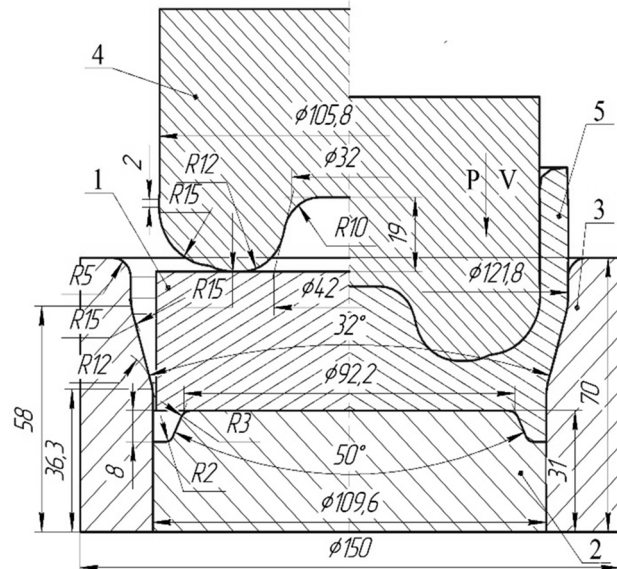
Схема зворотного видавлювання: 1 – заготовка; 2 – плита; 3 – матриця; 4 – пуансон; 5 – напівфабрикат
